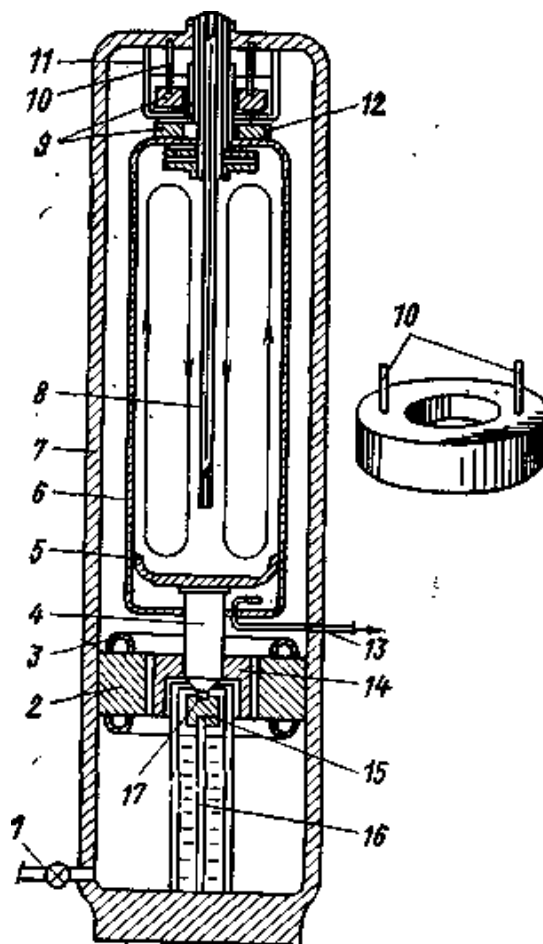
Газовая центрифуга (Нидерланды): 1 – трубка вакуумного насоса; 2 – статор электродвигателя; 3 – обмотка двигателя; 4 – опорный стержень; 5 – перегородка; 6 – ротор; 7 – корпус; 8 – трубка питания; 9 – магнитные тела; 10 – упругая связь; 11 – емкость с жидкостью (демпфер); 12 – молекулярное уплотнение; 13 – отборники фракций; 14 – ротор электродвигателя; 15 – маятник; 16 – упругий стержень; 17 – опорная сфера
